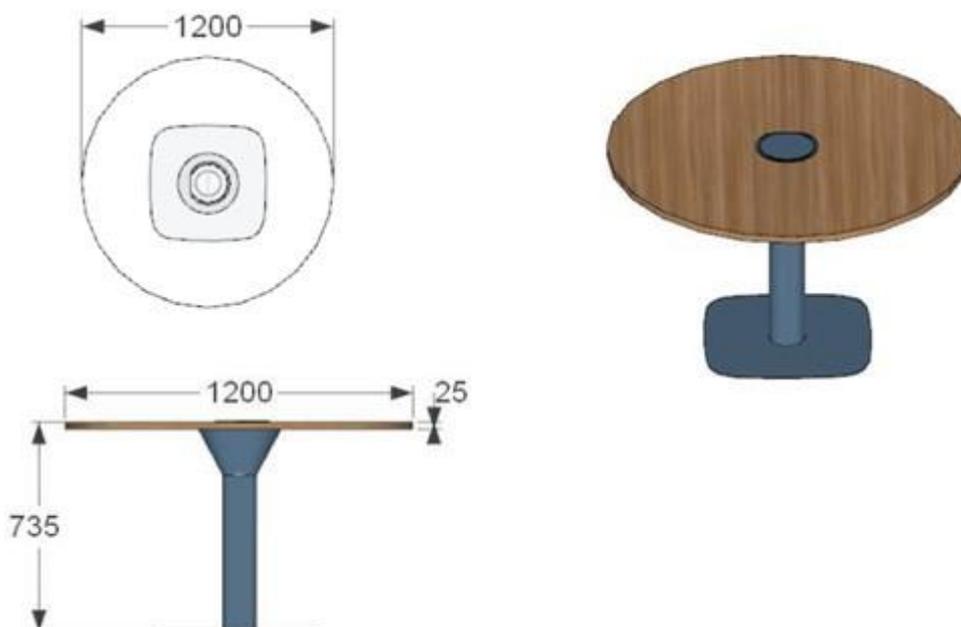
Planta baixa, vista frontal e perspectiva modelo item 20
